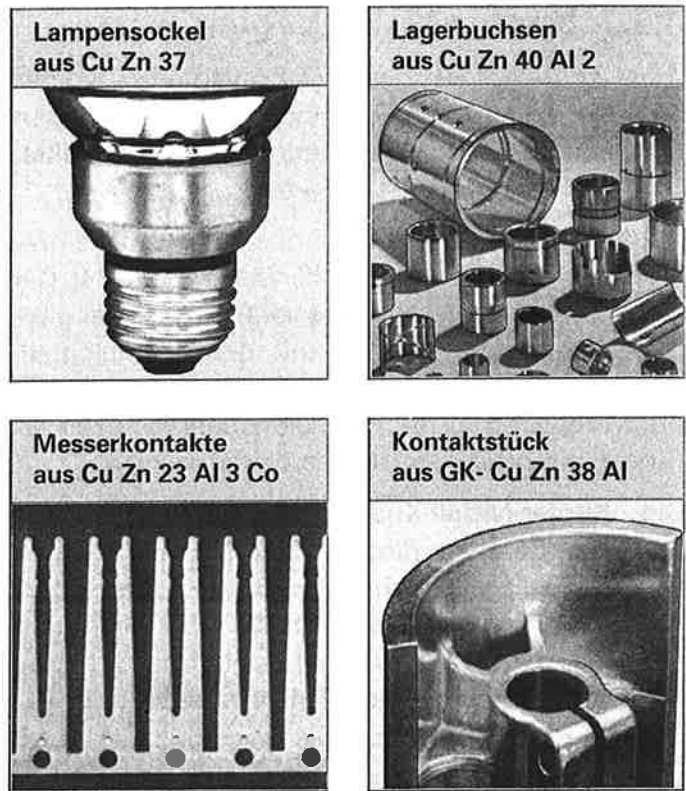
Bauteile aus Kupfer-Zink-Legierungen
